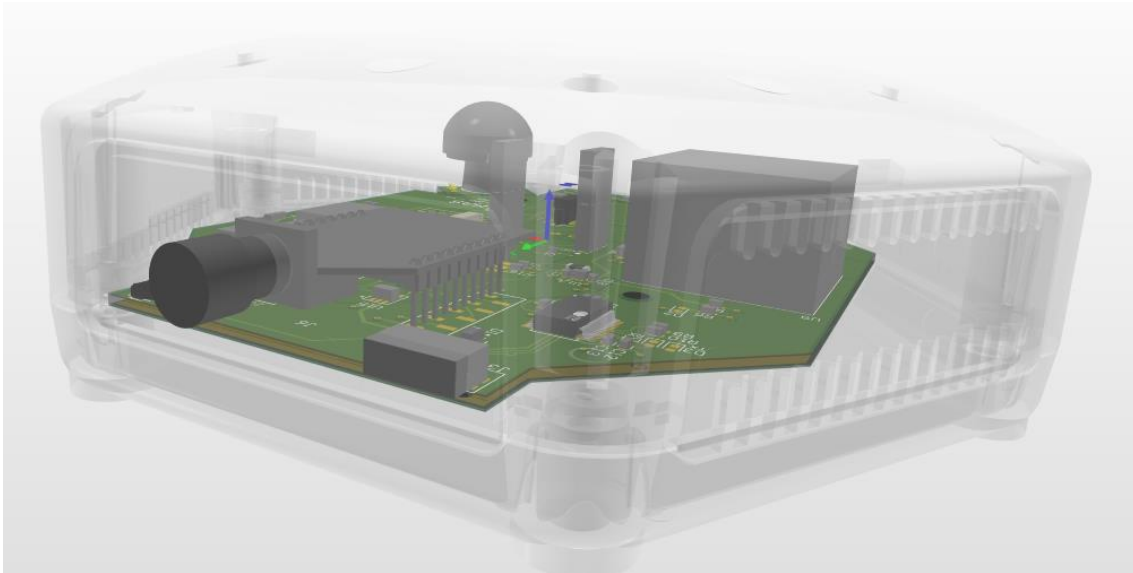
Vista lateral 3D de la PCB integrada en la caja
